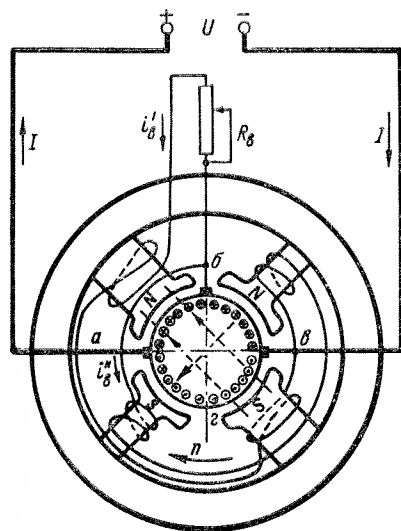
Сварочный генератор с расщепленными полюсами
